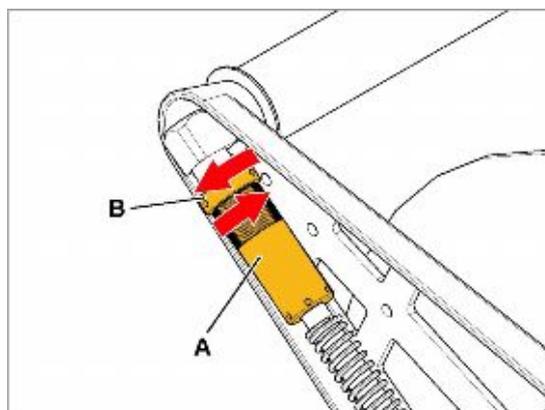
Регулировка силы восстановления пружины плавающего рычага на 400-мм размотчике
